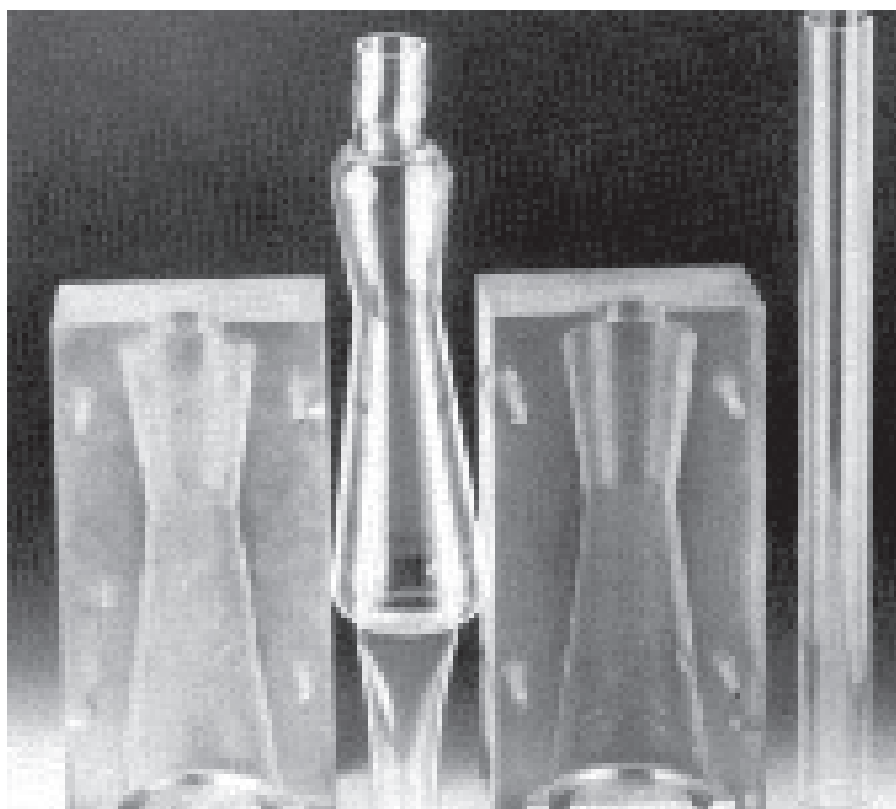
Formwerkzeug zum Aufweiten von Rohren mit Druckluft
